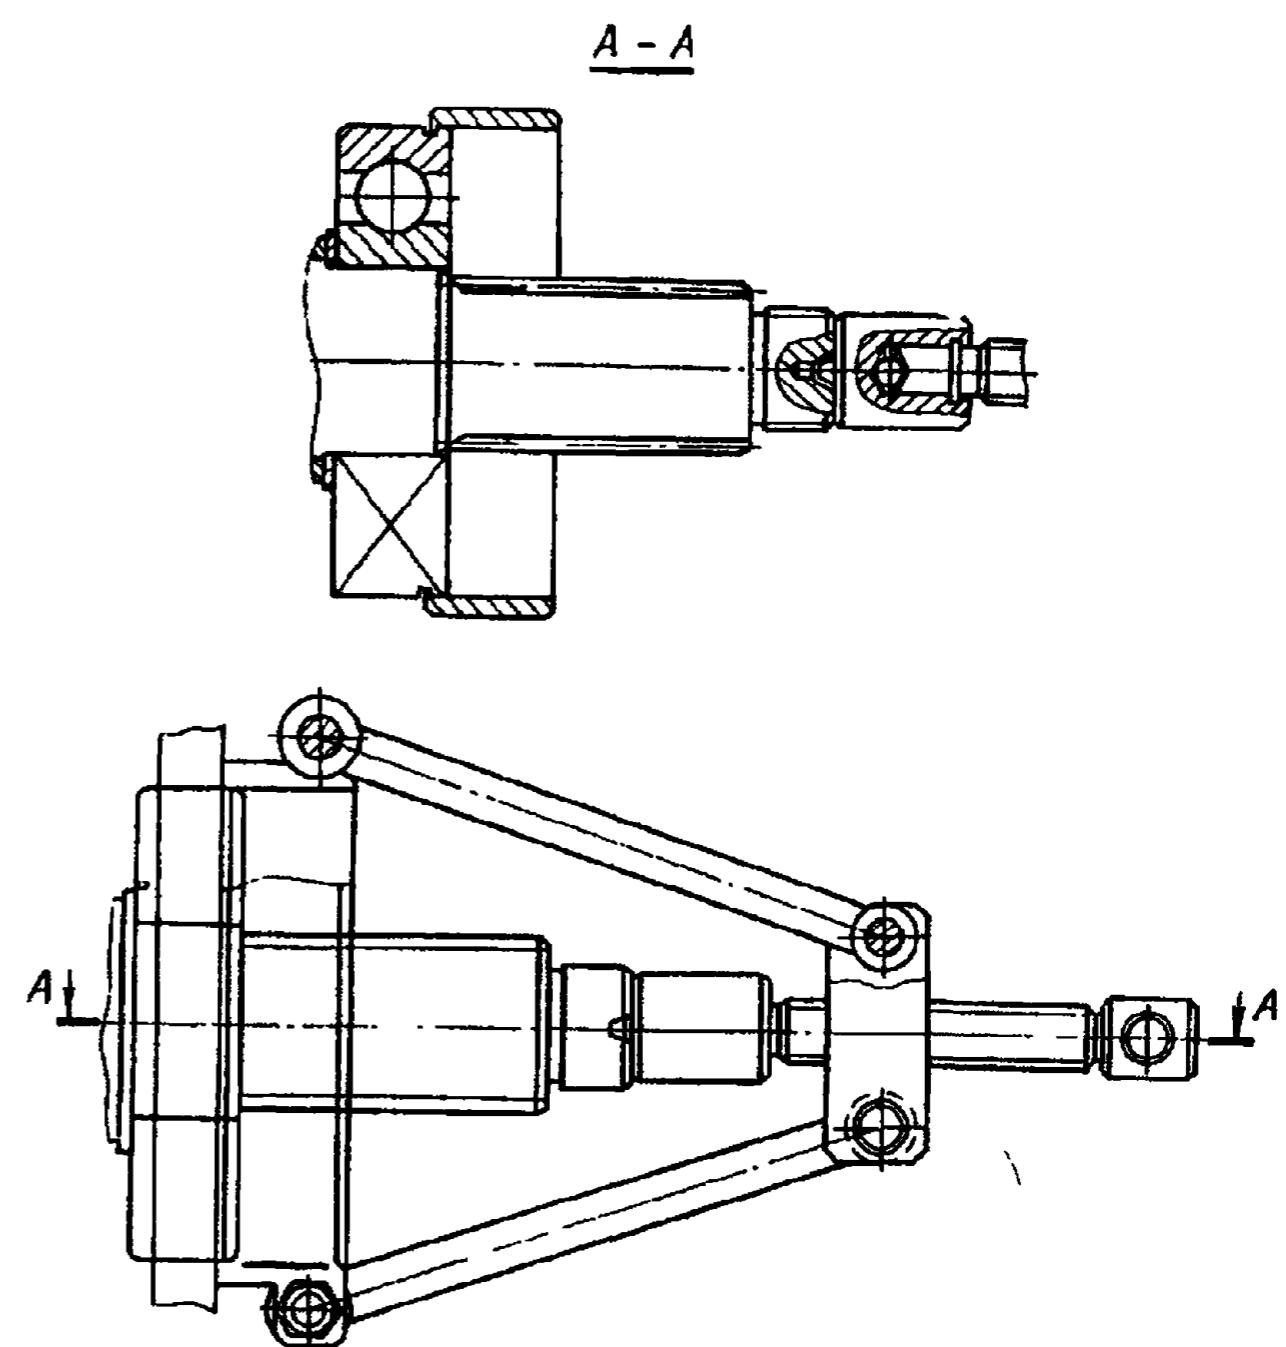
Снятие заднего подшипника ведущего вала съемником
